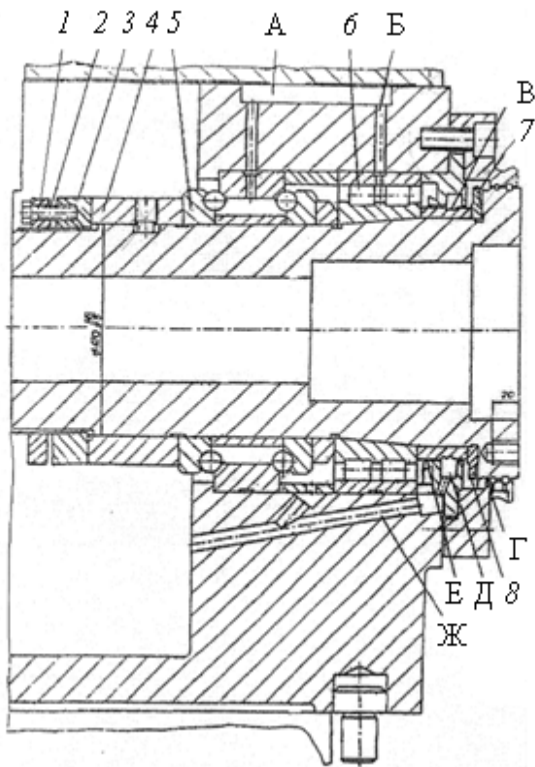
Передняя опора и конец шпинделя многоцелевого фрезерно-сверлильно-расточного станка
